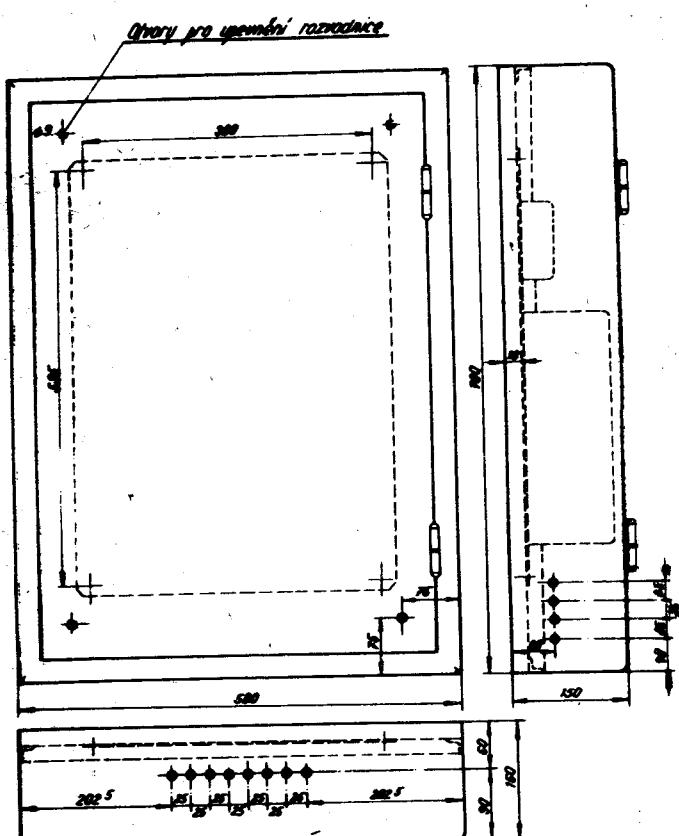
Základní deska se zesilovací soupravou TAZ 02 a montážními rozměry
